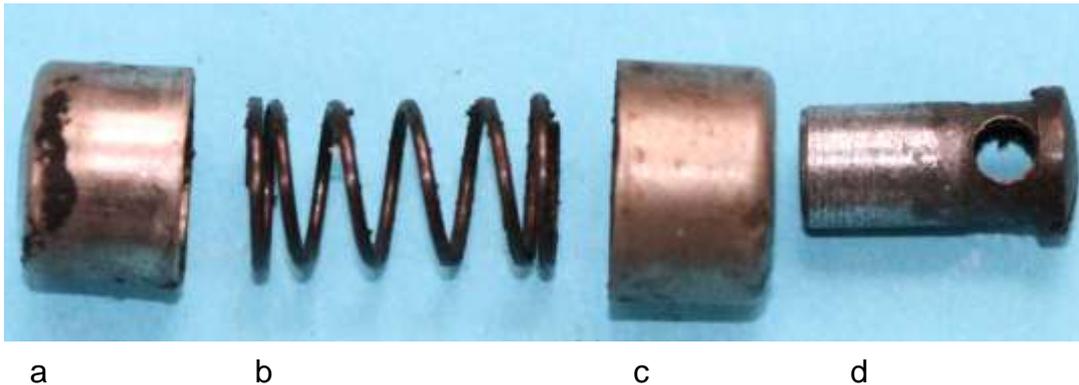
Federdruckklemme: a) Untere Kappe, b) Zylindrische Schraubenfeder, c) Obere Kappe, d) Schraube mit Innengewinde und Durchgangsbohrung für das Kabelende
